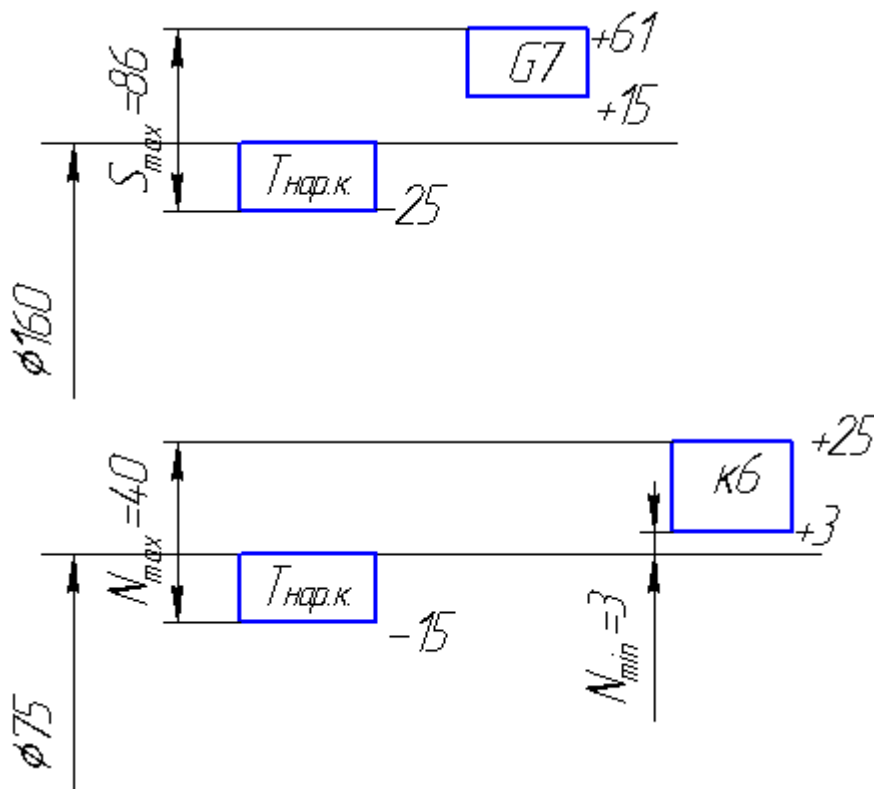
Схема расположения полей допусков посадочных размеров подшипников и сопряженных деталей.
